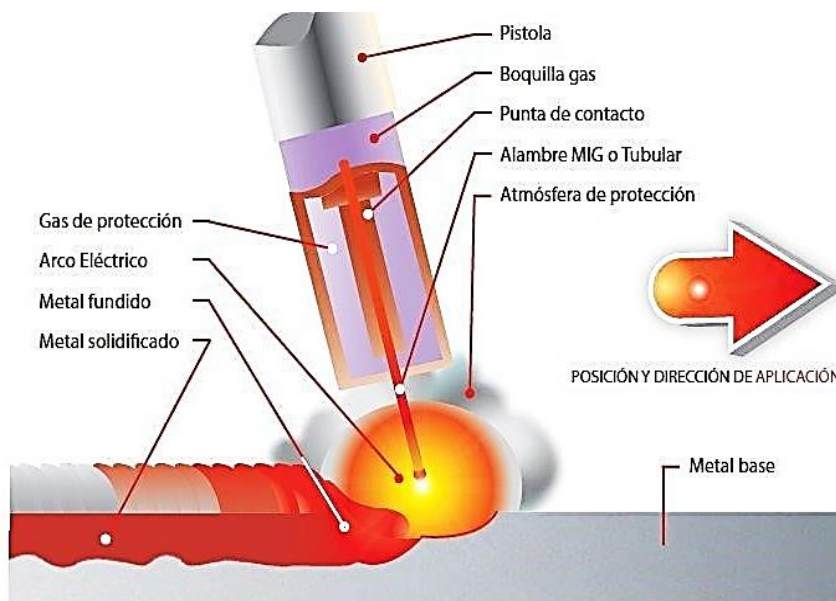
Proceso de soldadura MIG. Tomada de Pinterest
